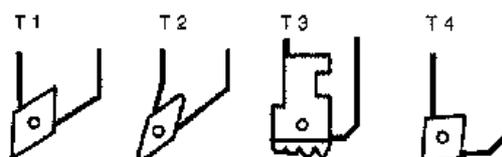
Herramientas de torneado: para desbaste, de acabado, para roscar, de acabado
